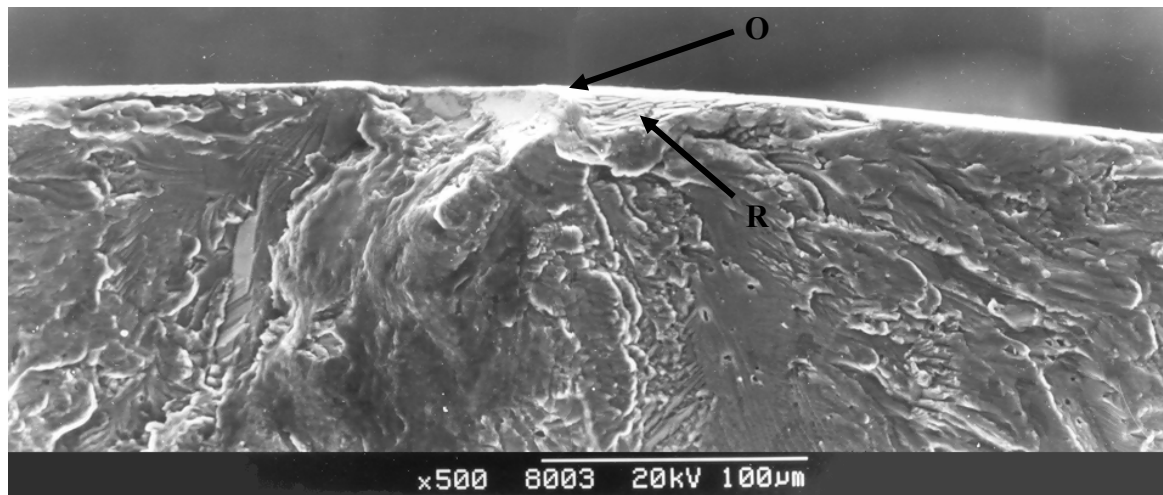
Ampliación del inicio de grieta en superficie de fractura de la probeta N° 1.
